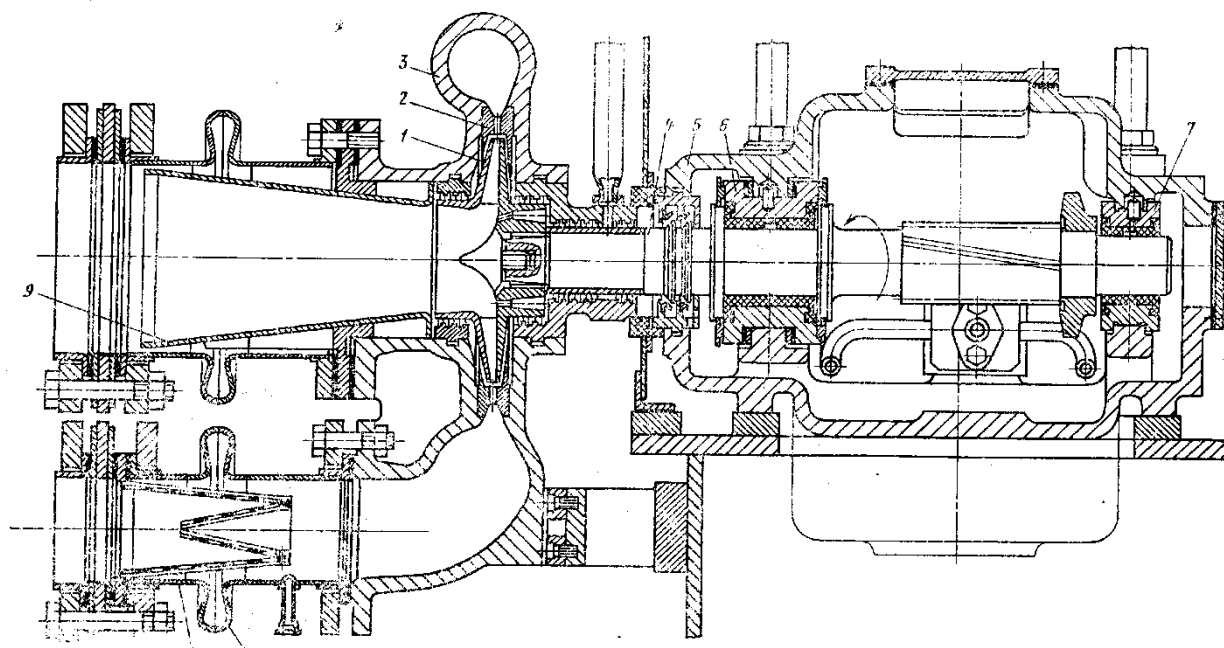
Воздушный одноступенчатый центростремительный ТД реактивного действия
